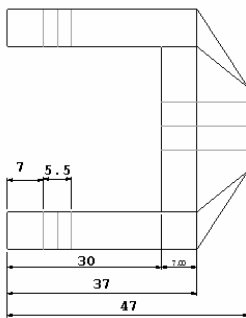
Disegno tecnico e dimensioni della staffa in millimetri
